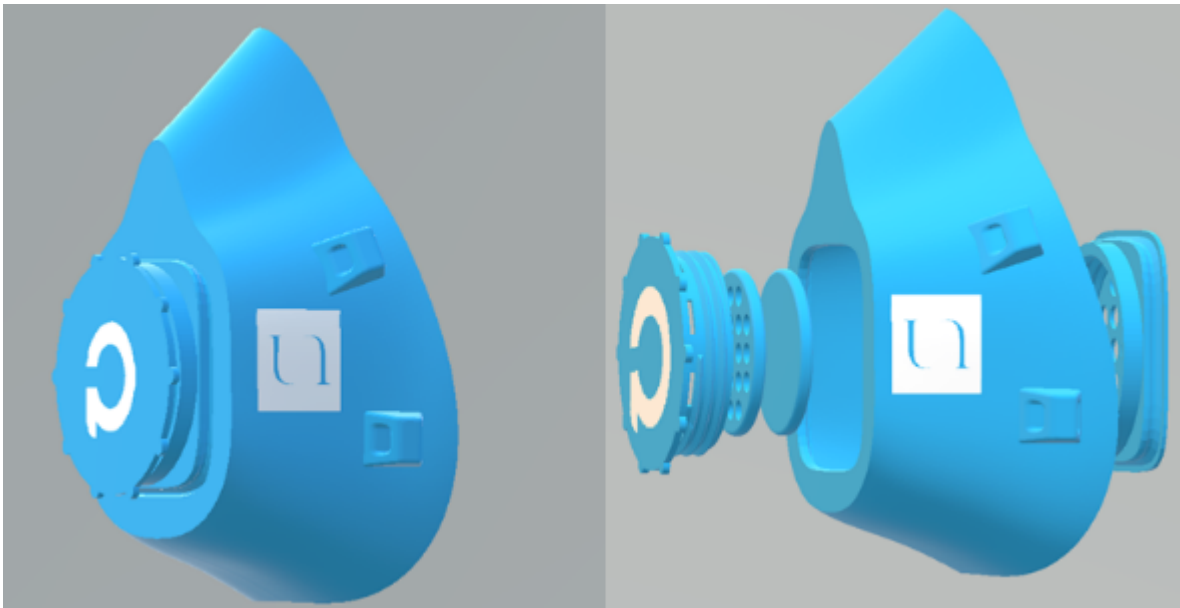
Masque connecté ; a : vue assemblée ; b : vue éclatée
